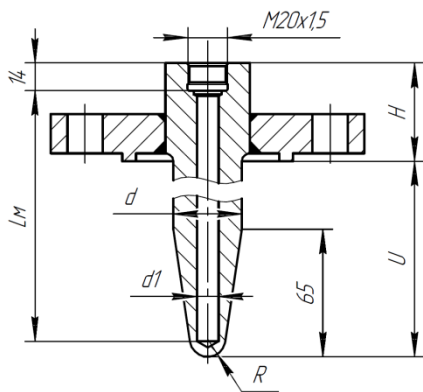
ГТ-704 для ДТ с подвижным штуцером
